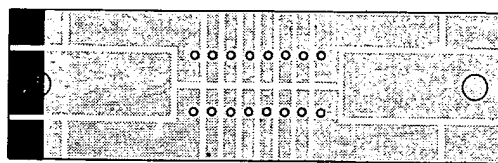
Deska s plošnými spoji části C z obr. 2 (L07)
